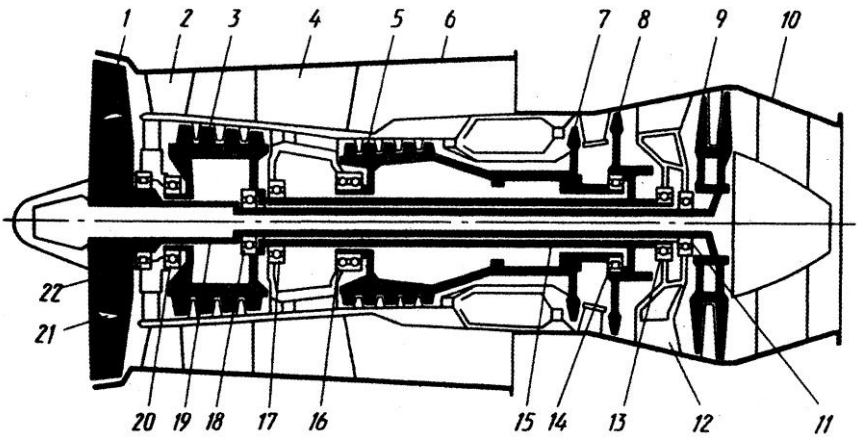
Трехвальный двухконтурный турбореактивный двигатель:
